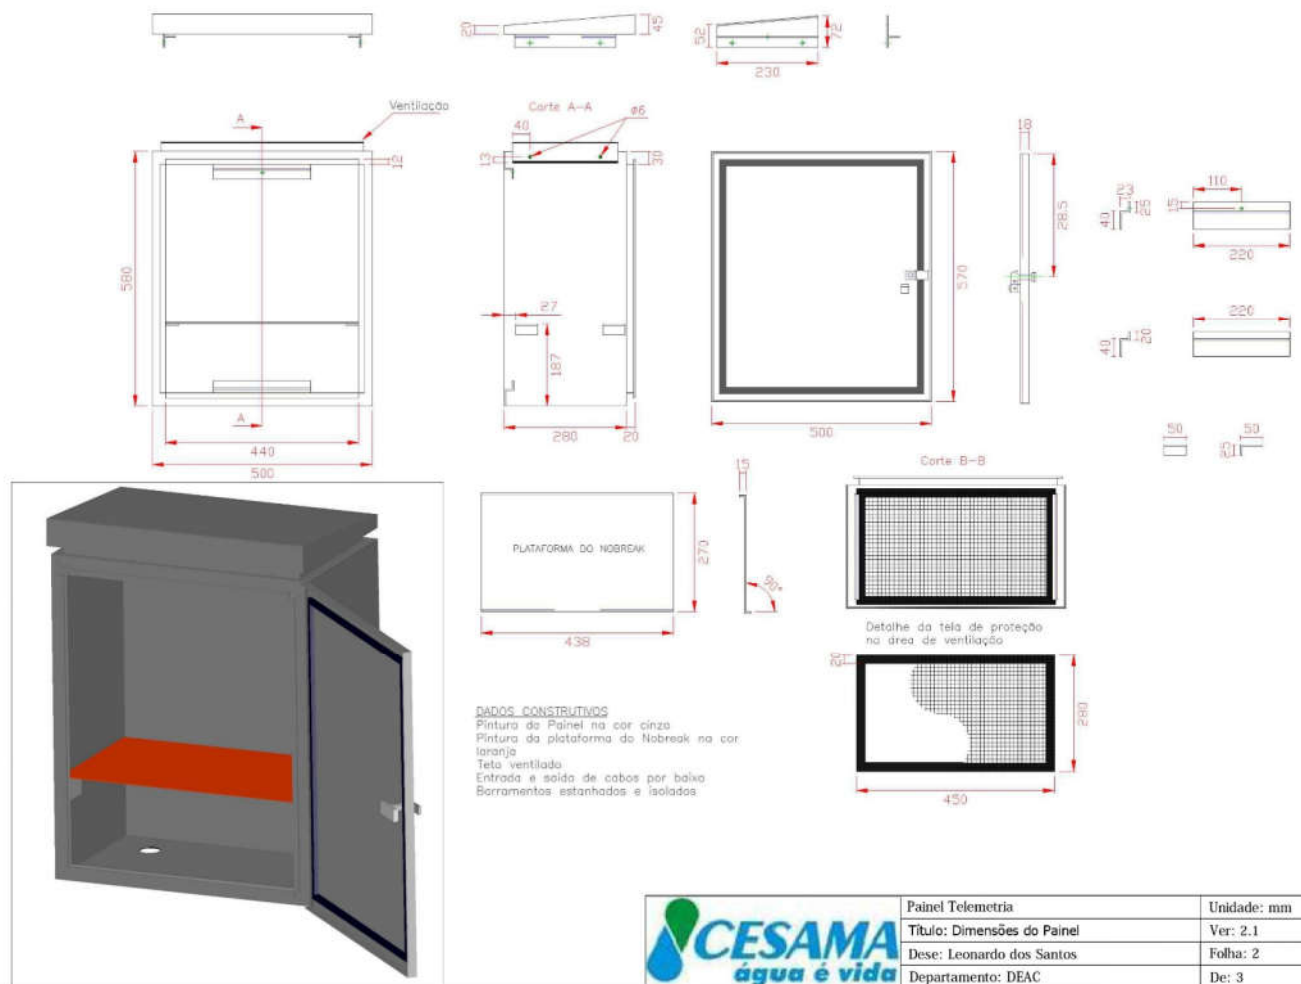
Detalhes construtivos painel de telemetria padrão CESAMA
